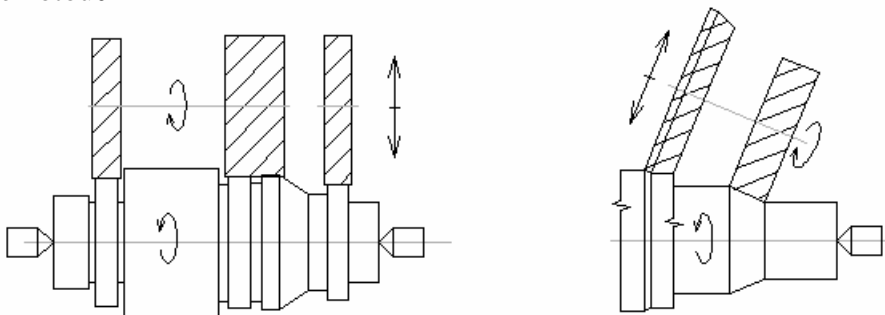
Zapichovací broušení jedním kotoučem [1]
